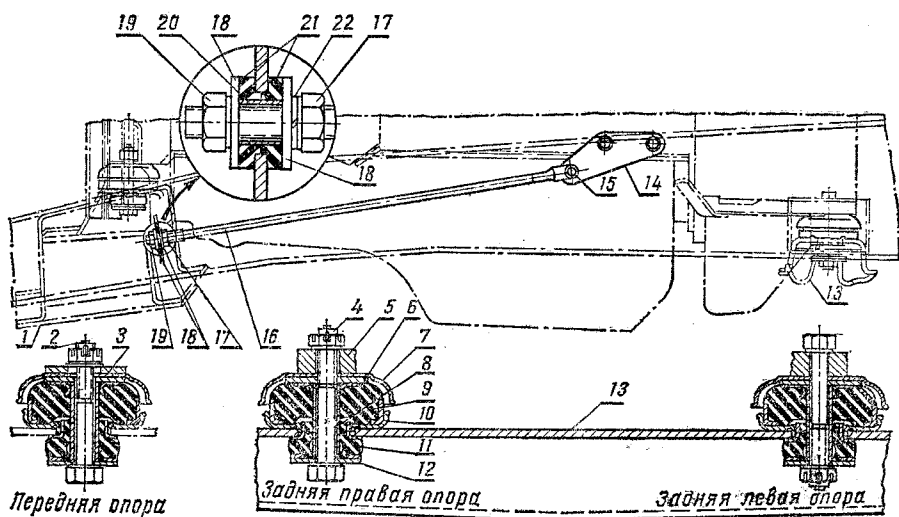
Крепление двигателя ГАЗ-52-01 к раме автомобиля:
